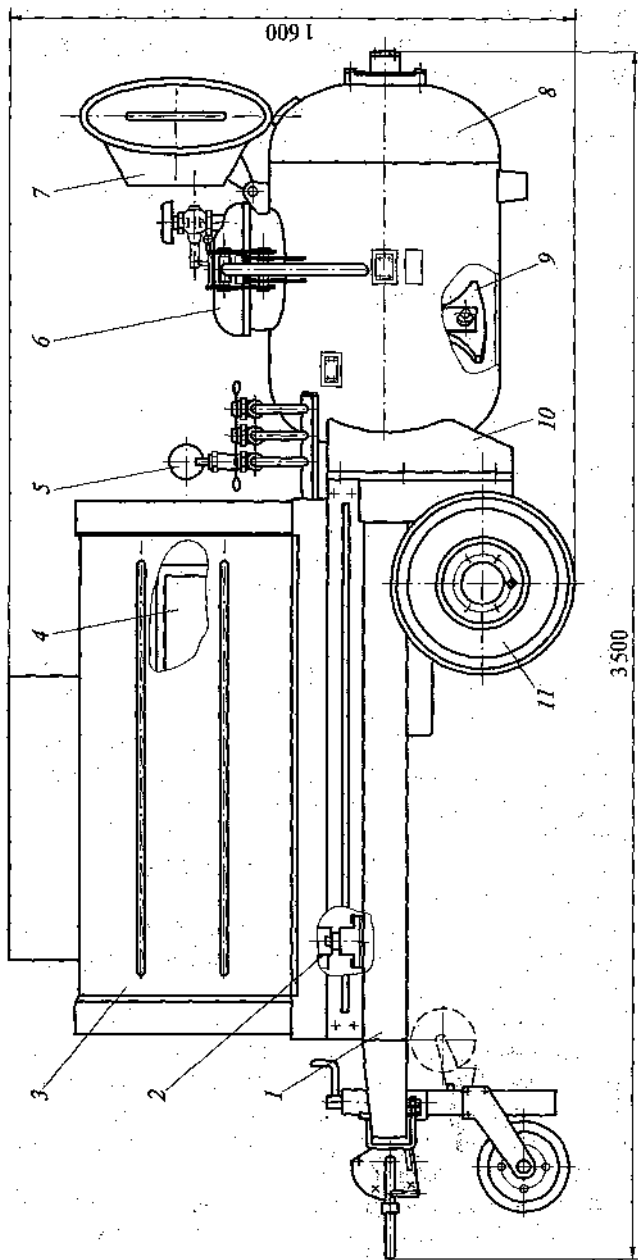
Установка для приготовления и подачи жестких растворов СО-165:
